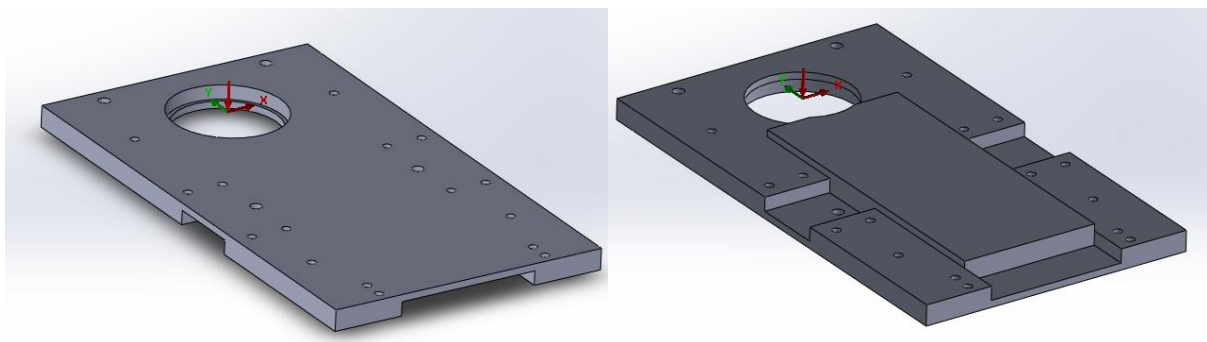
Sistemas de coordenadas de la parte fija del molde.
